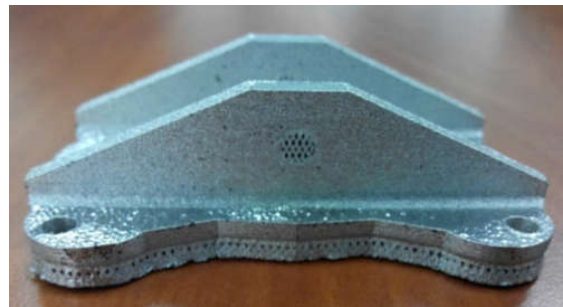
Заготовка кронштейна, напечатанная из материала Inconel625
